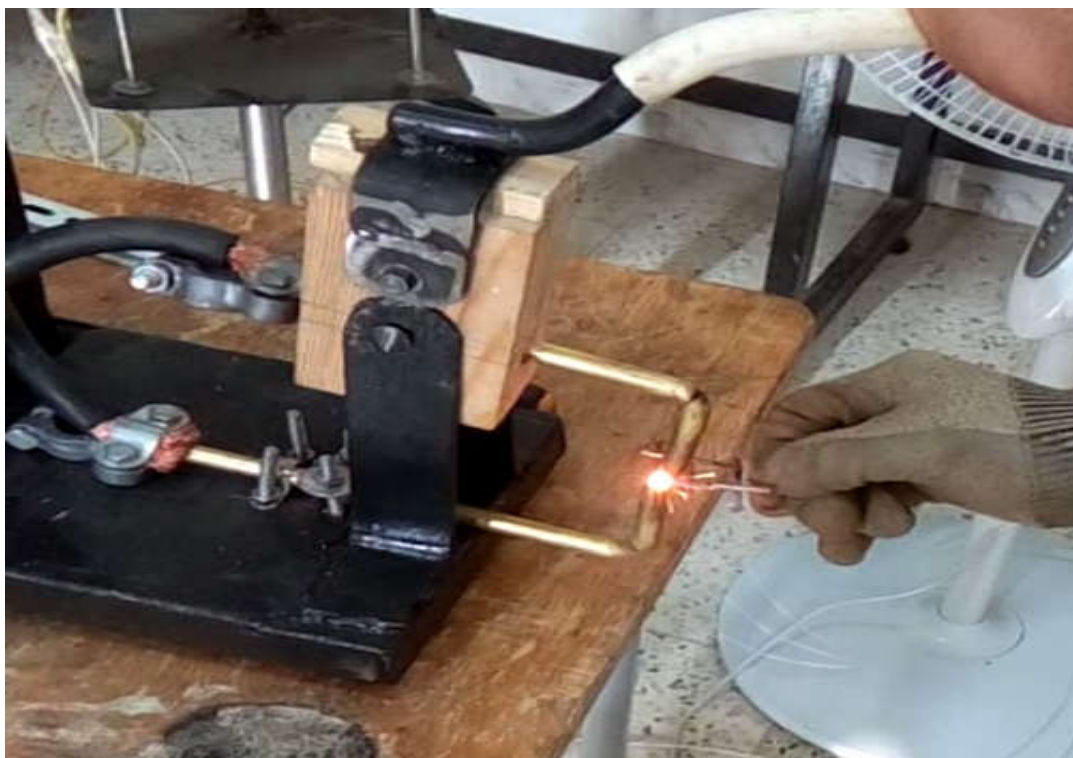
Presenté l'essai de soudage par points.
